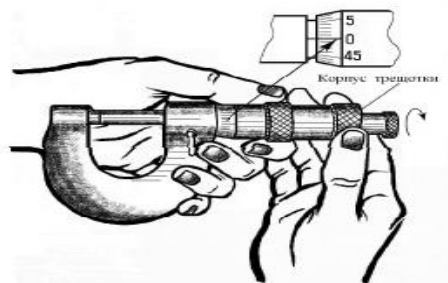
Установка барабана и завинчивание корпуса трещотки
